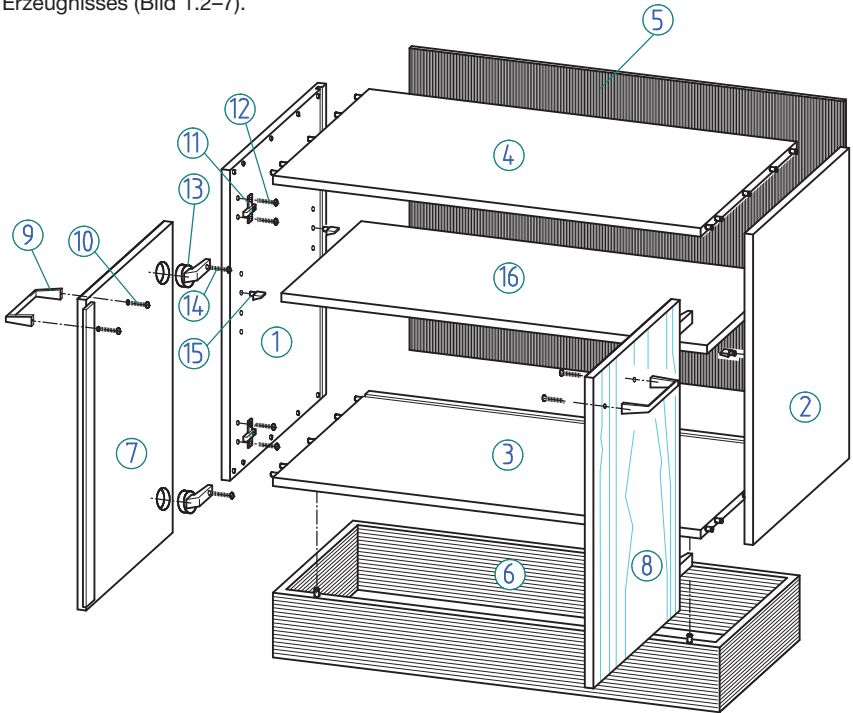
Zusammenbau-Zeichnung als Explosionszeichnung
